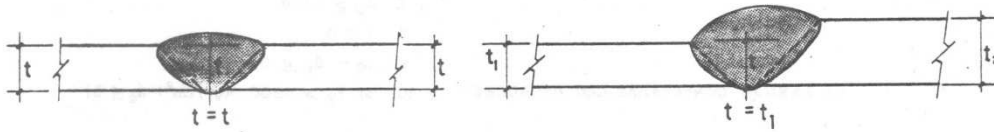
ESPESORES EFECTIVOS DE LAS SOLDADURAS
